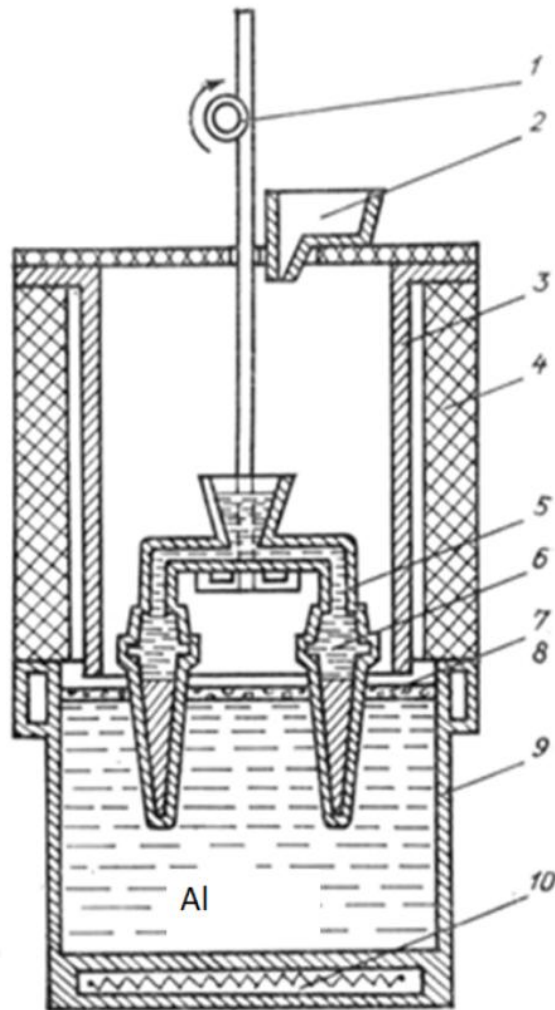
Схема ливарної установки УВНК-8П (1 — механізм опускання форми у рідкометалевий охолоджувач; 2 — чаша для зливу розплавленого металу у форму; 3 — піч підігріву форм (ППФ); 4 — теплоізоляція; 5 — оболонкова форма, виготовлена із вогнетривкої суміші на основі білого електрокорунду; 6 — робочий сплав; 7 — теплозахисний екран, що складається із керамічних гранул; 8 — рідкометалевий охолоджувач; 9 — місткість рідкометалевого охолоджувача; 10 — піч підігріву рідкометалевого охолоджувача)[61]
